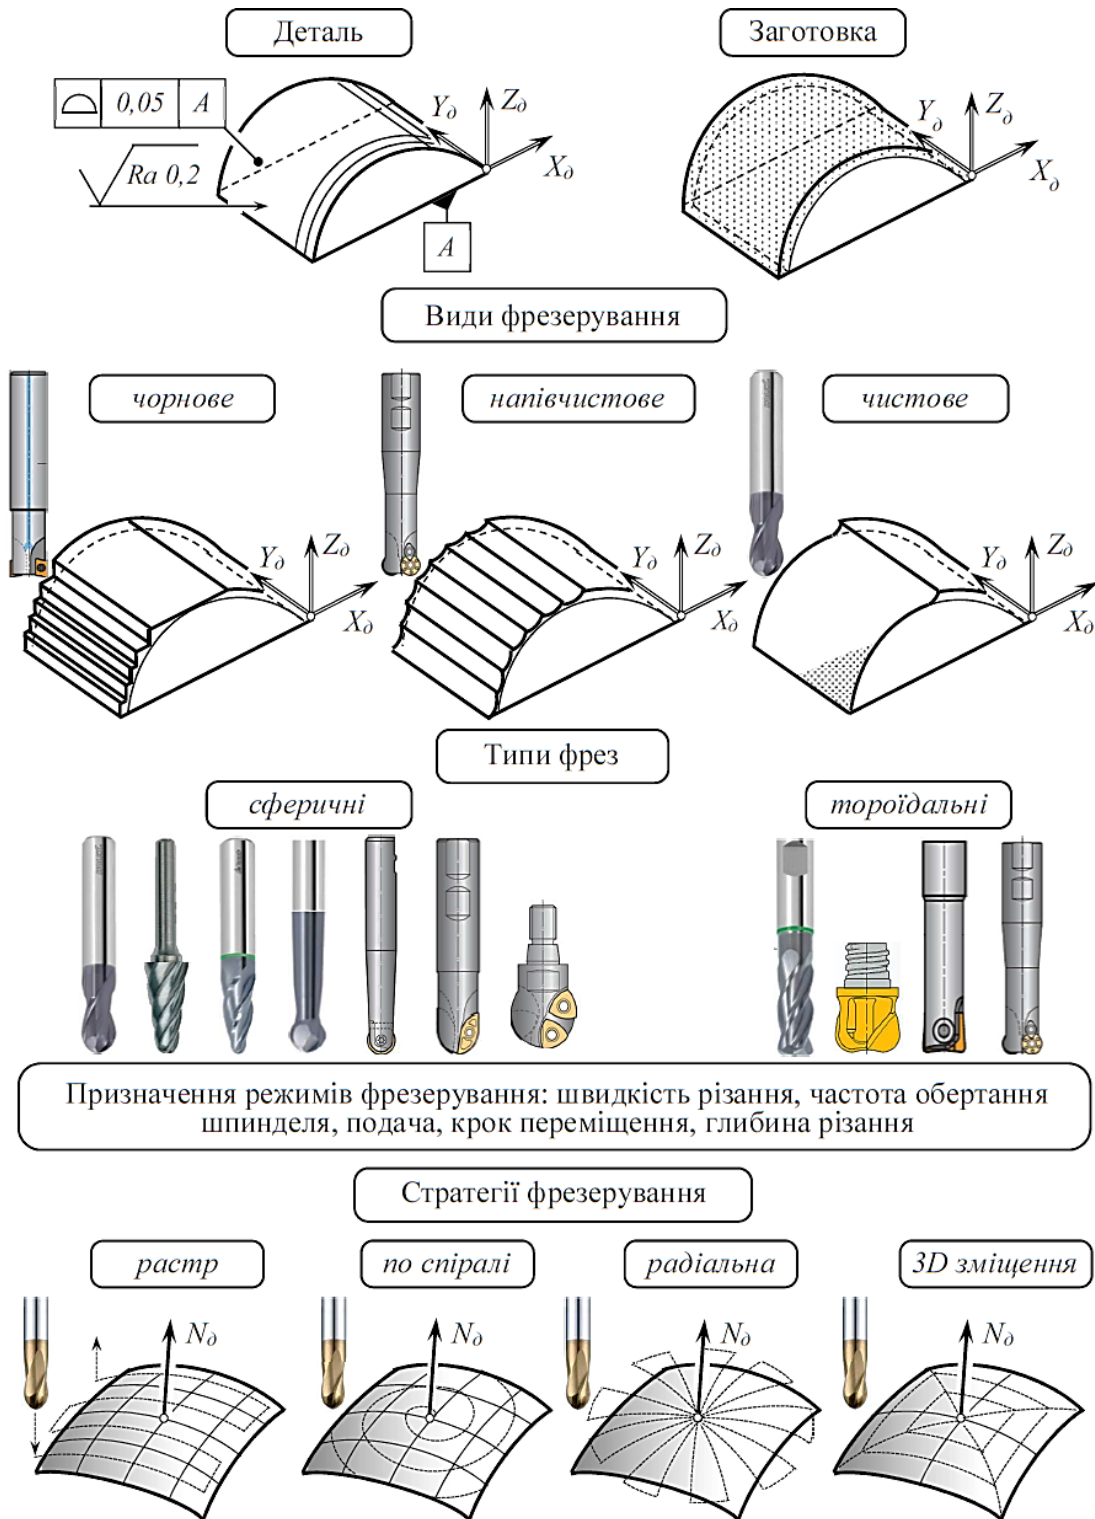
Етапи технологічної підготовки фрезерування деталей з криволінійними фасонними поверхнями
